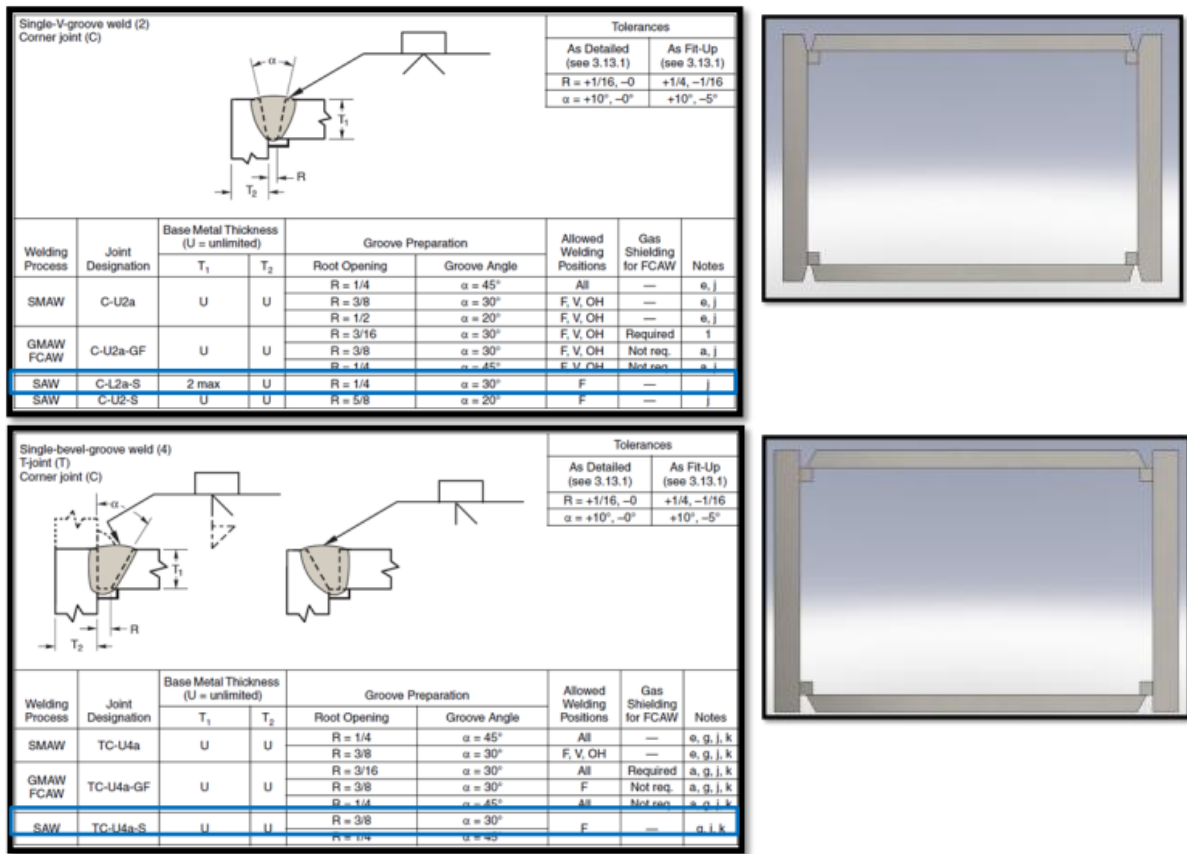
Diseño de junta para desarrollo experimental acorde a AWS (Sociedad Americana de Soldadura, por sus siglas en inglés)
